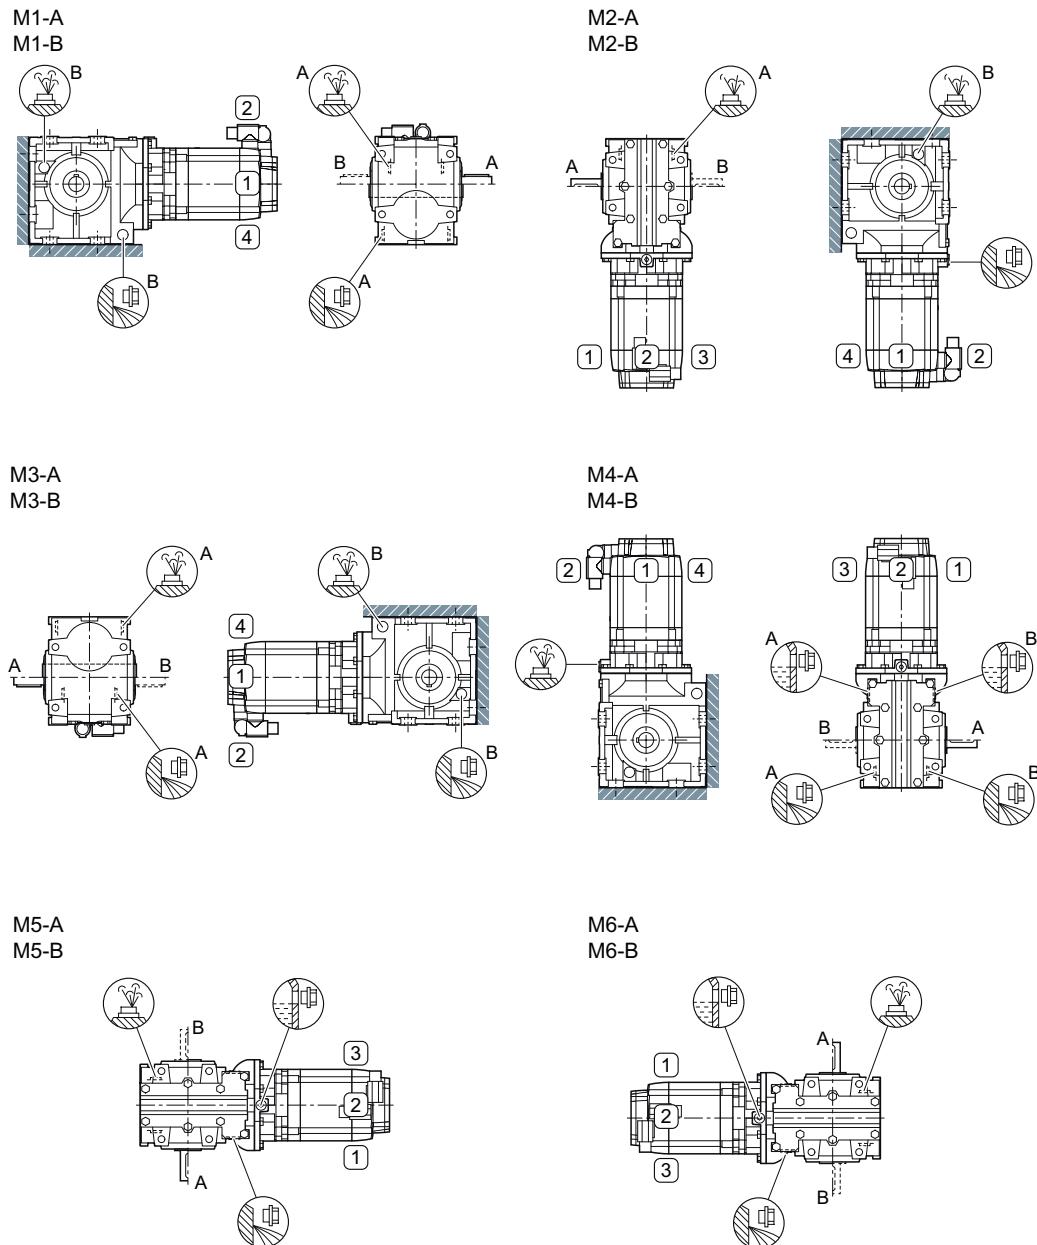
Einbaulagen für Servo-Stirnradschneckengetriebemotor C, Fußausführung, Baugrößen 29, 2-stufig
